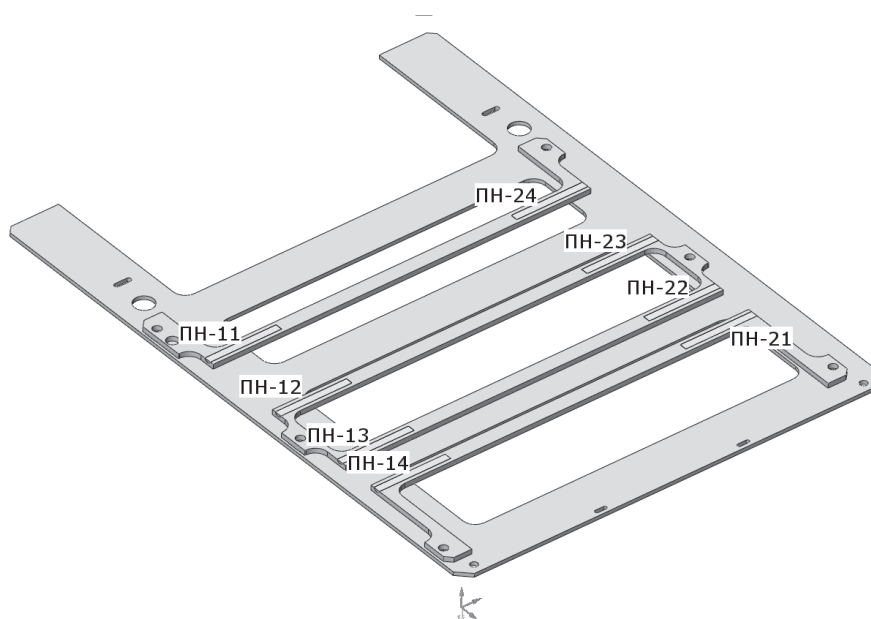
Разрез основания корпуса и патронные нагреватели.
